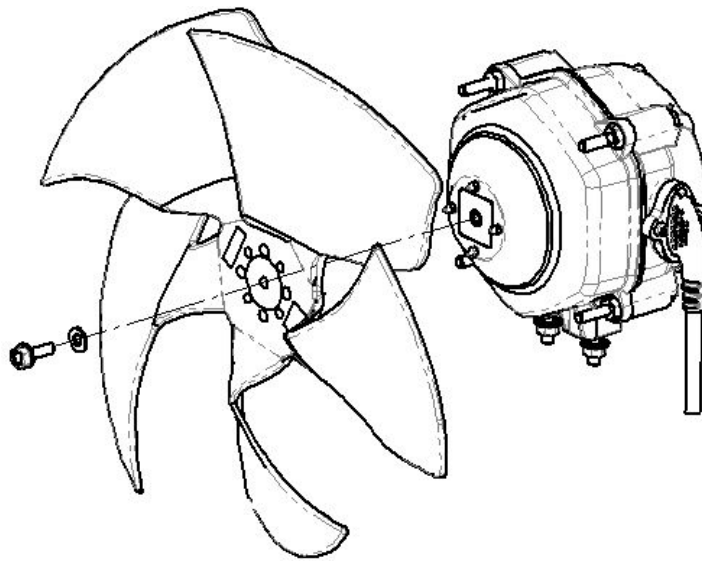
Ensamblado del ventilador (eje de rosca interna). Ajuste del par de torsión: 1,5 – 1,7 Nm
